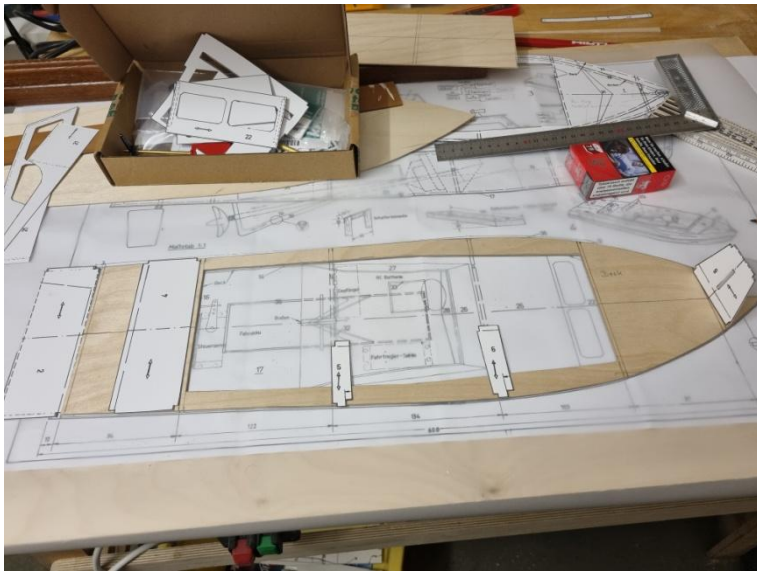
Auch der Decksausschnitt ist fertiggestellt
